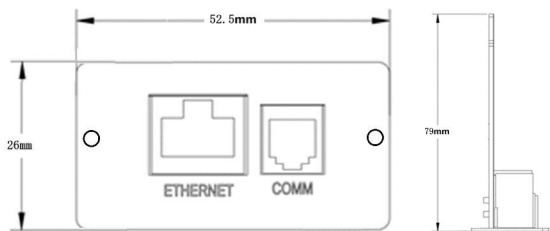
Чертеж конструктивных размеров.
